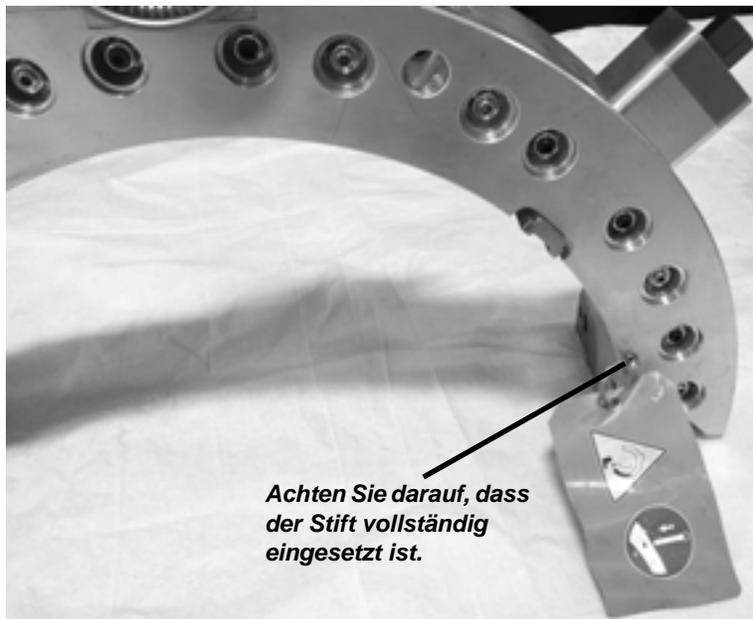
Beim Heben oder Handhaben einer getrennten Maschine müssen die Ausrichtungsstifte immer eingesetzt sein.
